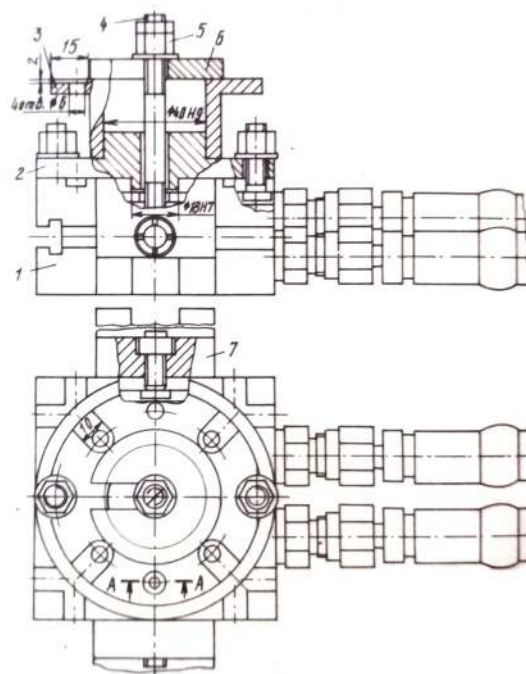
Механизированное УСП-8 для фрезерования четырех пазов и сверления четырех отверстий во фланце на станках с ЧПУ
